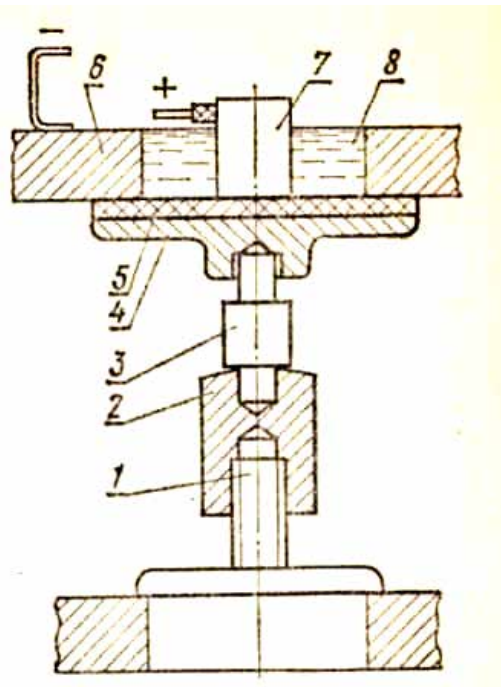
Відновлення поверхні посадочного отворів в корпусі: 1 - гвинт з фланцем; 2 - гайка, 3 - упорний стрижень, 4 - диск, 5 - ізоляційна (гумова) прокладка; б - корпус коробки передач (катод); 7 - анод, 8 - ванна в відновлюваному отворі .
